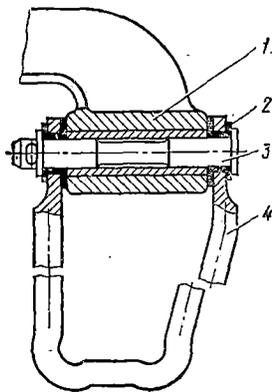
Крепление подвески тормозного башмака грузового вагона на боковой раме тележки:
